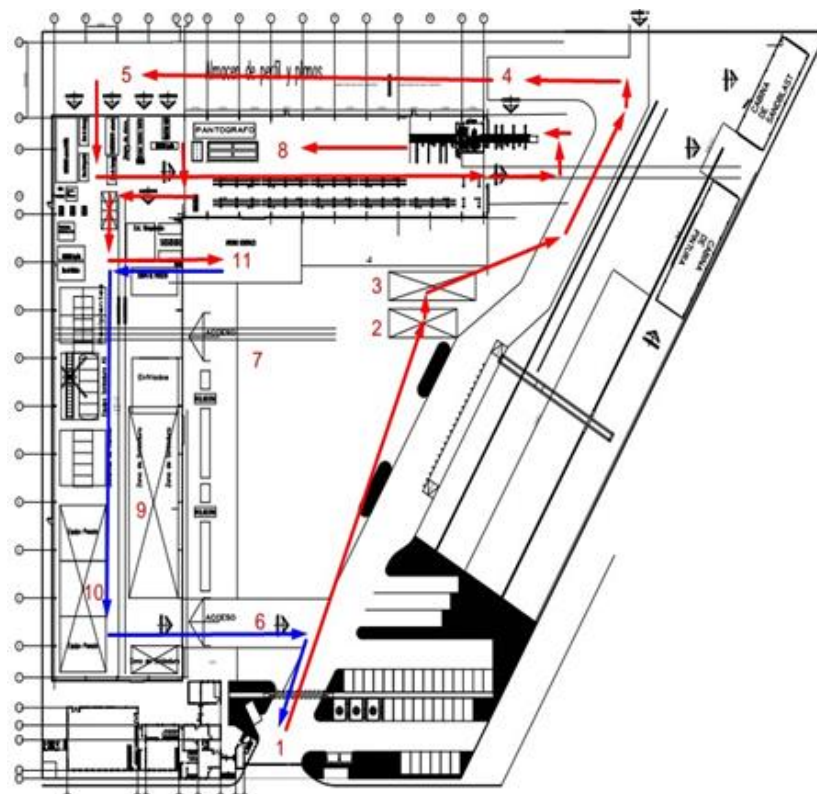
Layout prueba 5 de la Planta Durosa Santa Rosa SA, de CV.
